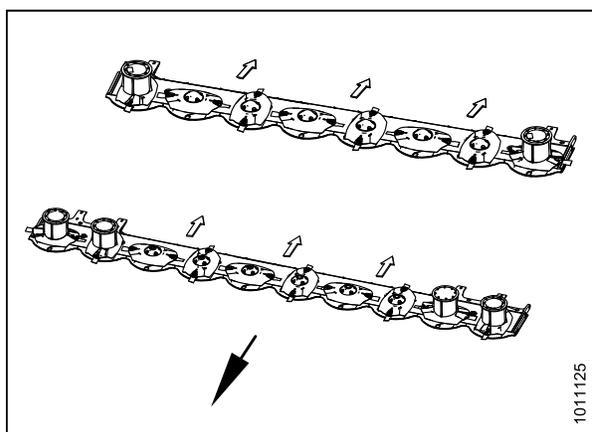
Barres de coupe de 4 et 4,9 m (13 et 16 pi)
